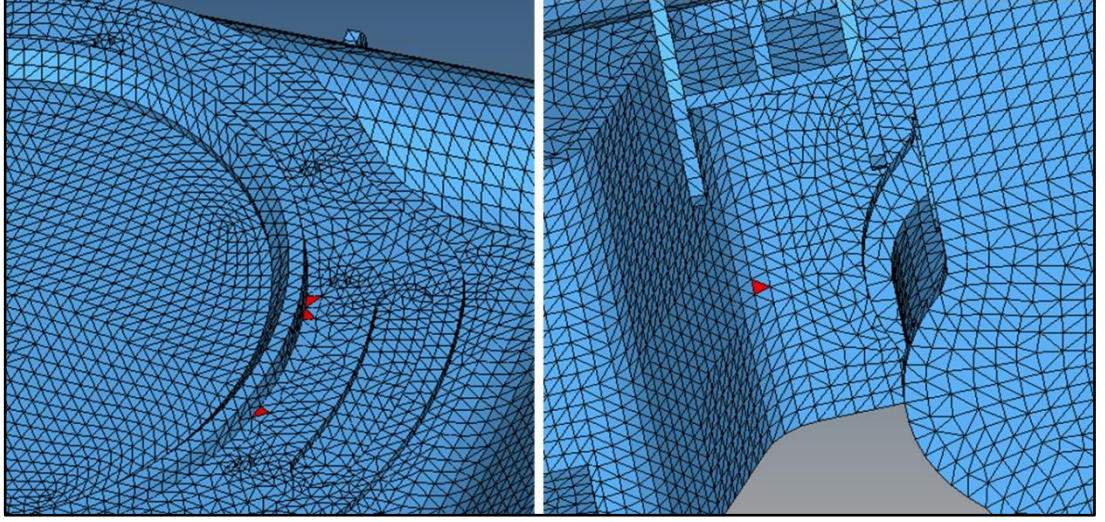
Bolster bölgesinde kritik kesitler.
